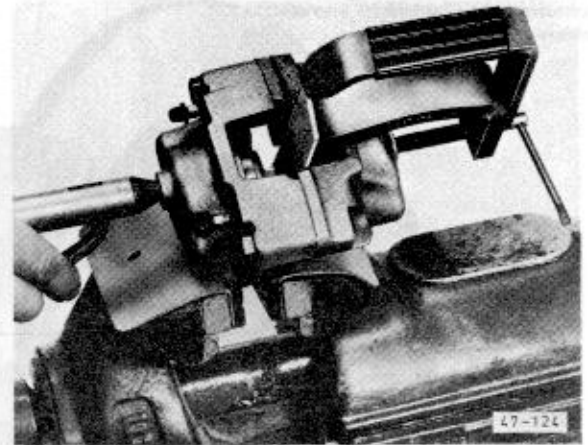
Kolben mit Druckluft aus dem Zylinder drücken
